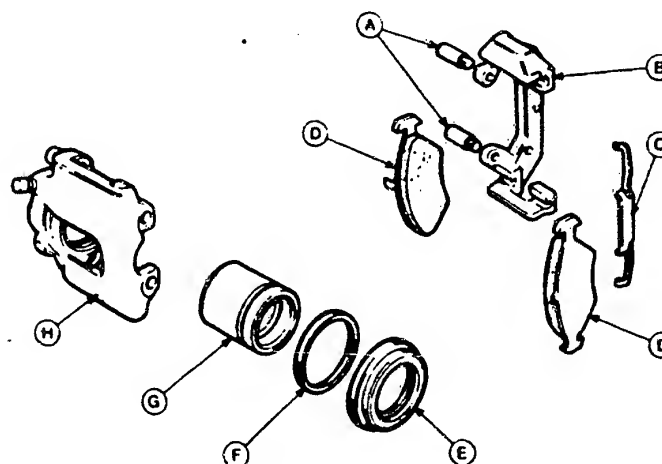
Bremssattel vorne: A Befestigungsschrauben – B Bremsklotzträger – C Halteklammer – D Bremsklötze – E Staubmanschette – F Kolbendichtung – G Kolben – H Kolbengehäuse.
